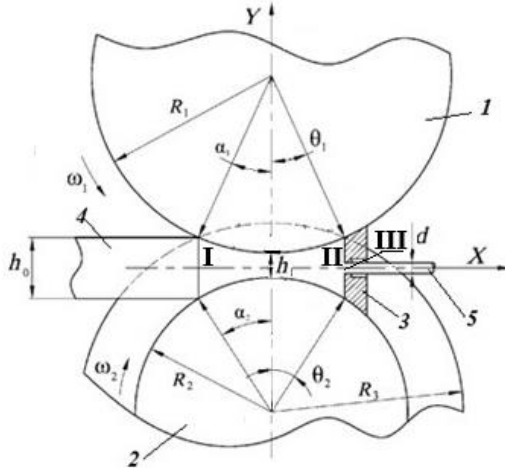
Схема очага деформации процесса СПП с одним приводным валком: 1 – валок в выступом; 2 – валок с канавкой, 3 – матрица; 4 – заготовка; 5 – проток; I – зона прокатки; II – зона распрессовки; III – зона прессования
